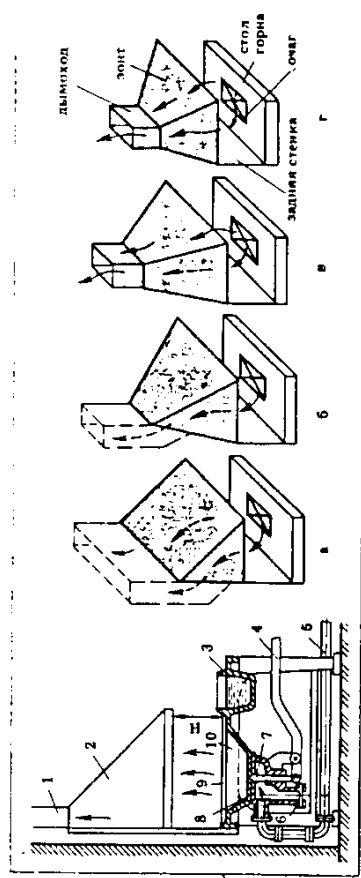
Оборудование для нагрева заготовок: стационарный металлческий горн (слева): 1 — выгнанная труба; 2 — зонт; 3 — бочок с водой для охлаждения инструмента; 4 — рычаг для регулирования подачи воздуха; 5 — воздухопровод; 6 — заслонка; 7 — конический наконечник; 8 — фурма; 9 — литой стол; 10 — очаг; типы зонтов (справа): а, б — дымоход в стене; в — наружный боковой дымоход; г — наружный центральный дымоход
